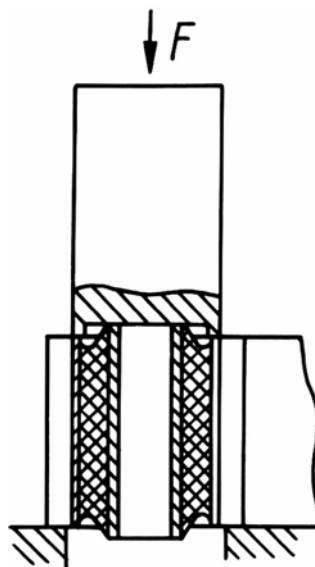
Выпрессовка шарнира из ушка рессоры
